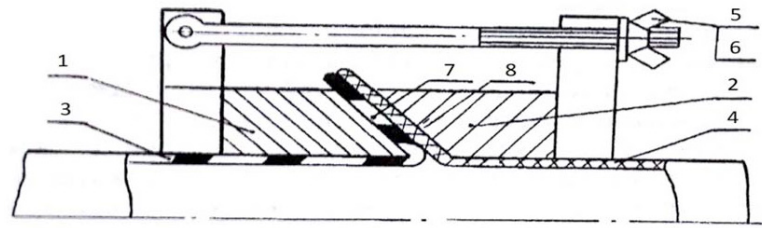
Соединение вентиляционных труб СВТ-1
